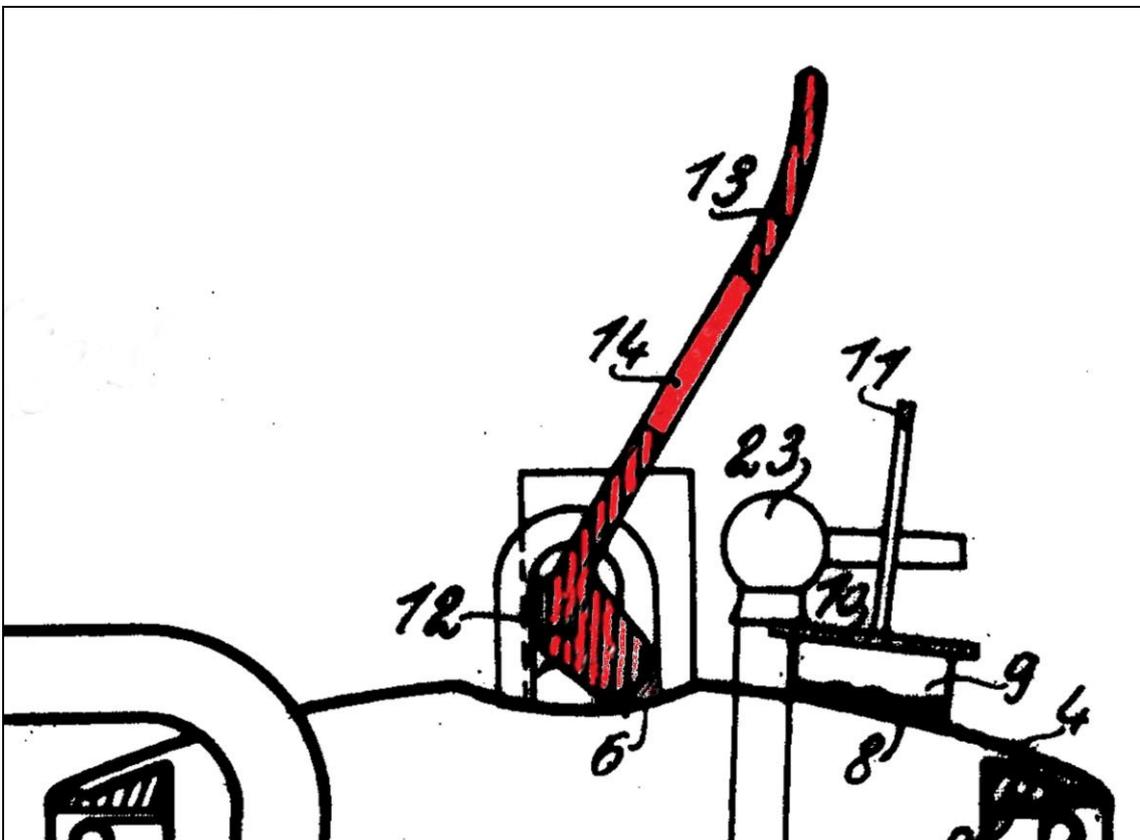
Detalle de la solapa de cierre (Arch. J.M. Sanchis).
